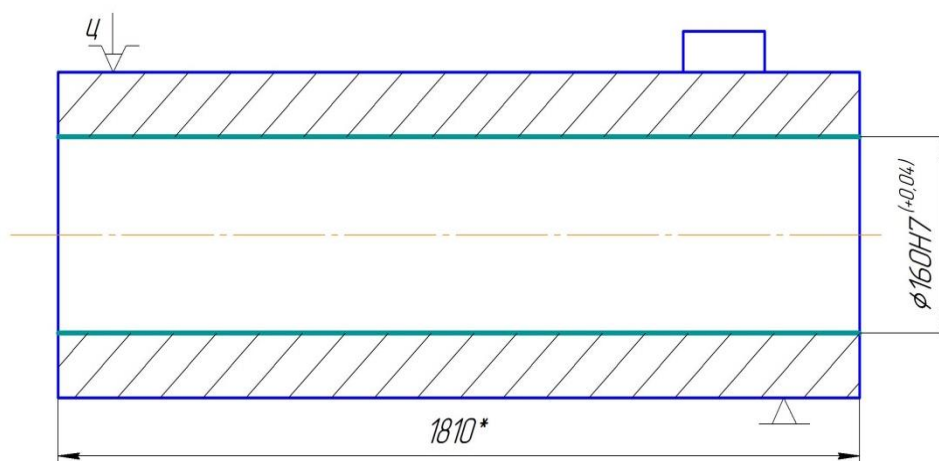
Эскиз детали и схема установки при раскатывании внутренней поверхности
